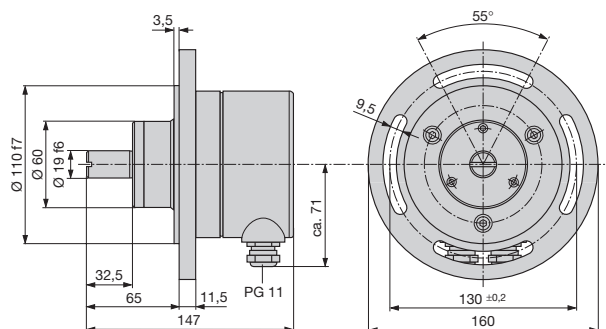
KINAX WT 707 mit Schraubklemmen sowie Stopfbuchsen und Flansch.
